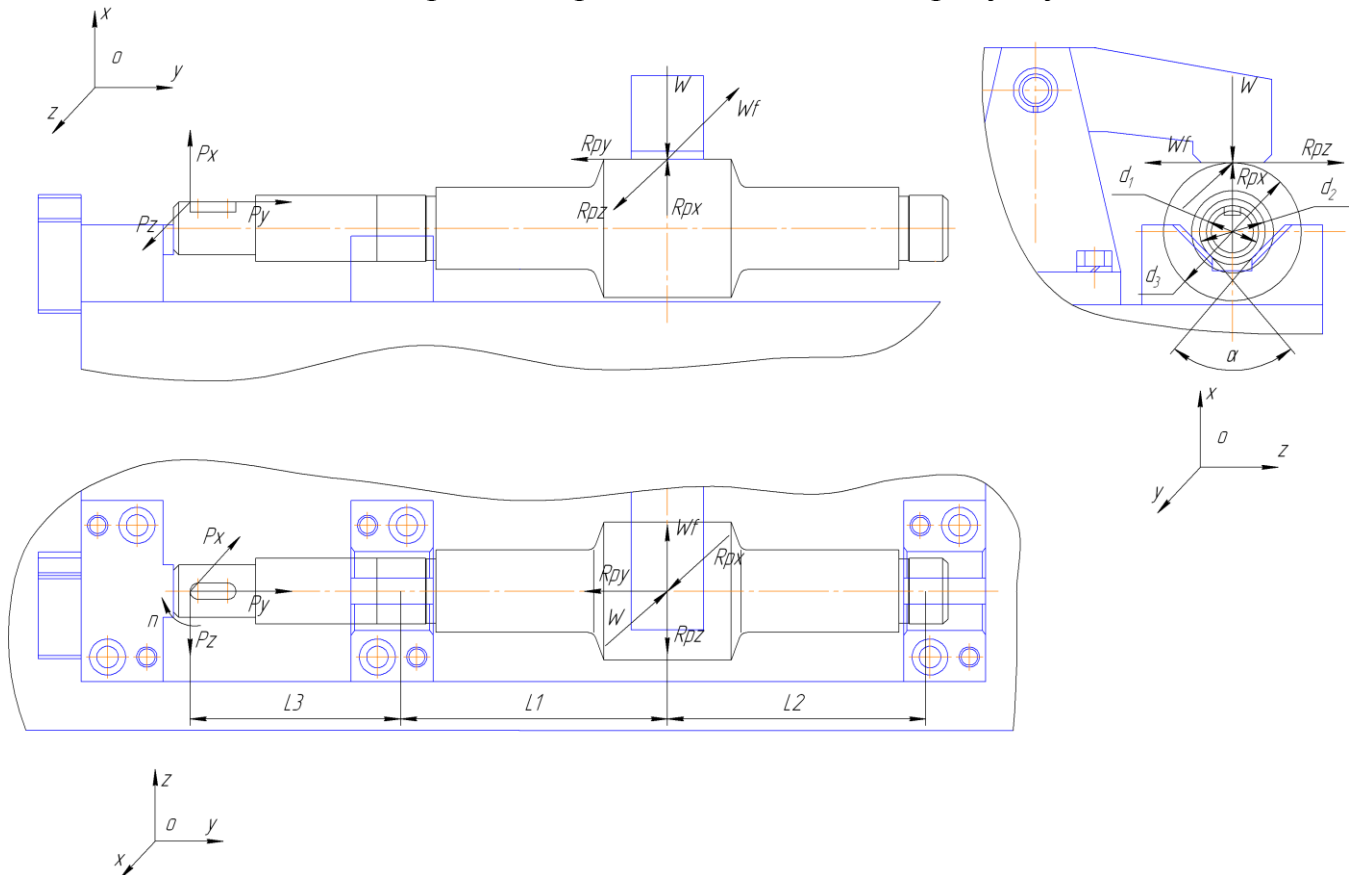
Схема сил, діючих на деталь при фрезеруванні паза 5P9<sup>(-0,012 / -0,042)</sup>
